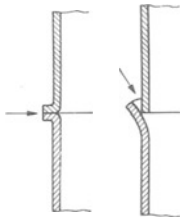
Bördel- und Kelchschweißnähte.
